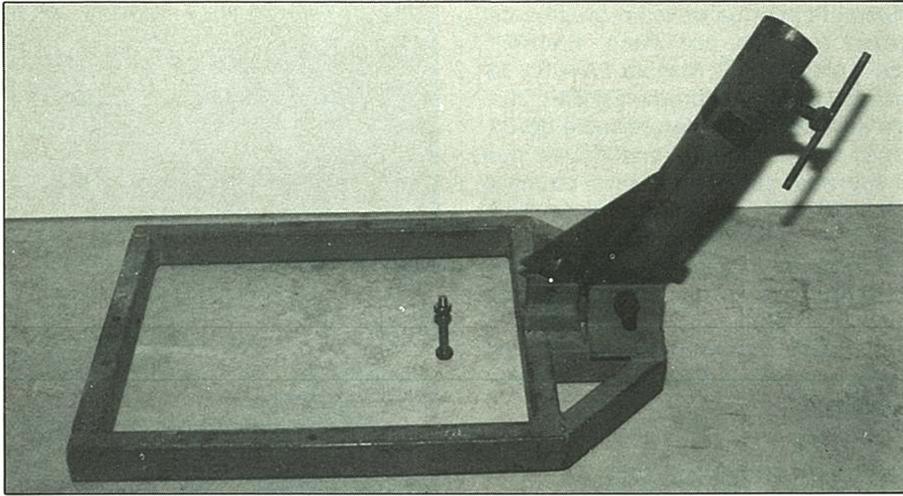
Vista del soporte. El tubo de alojamiento del mástil aparece inclinado.
